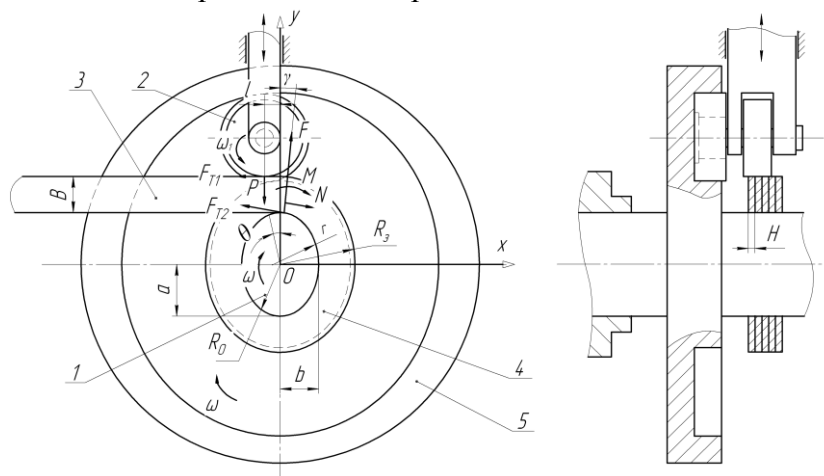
Розрахункова схема процесу формоутворення еліпсної навивної заготовки на оправу: 1 – еліпсна оправа; 2 – притискний ролик; 3 – стрічка; 4 – гвинтовий еліпсний елемент заготовки; 5 -торцевий кулачок, форма якого відповідає еквідистанті еліпсної оправи 1
